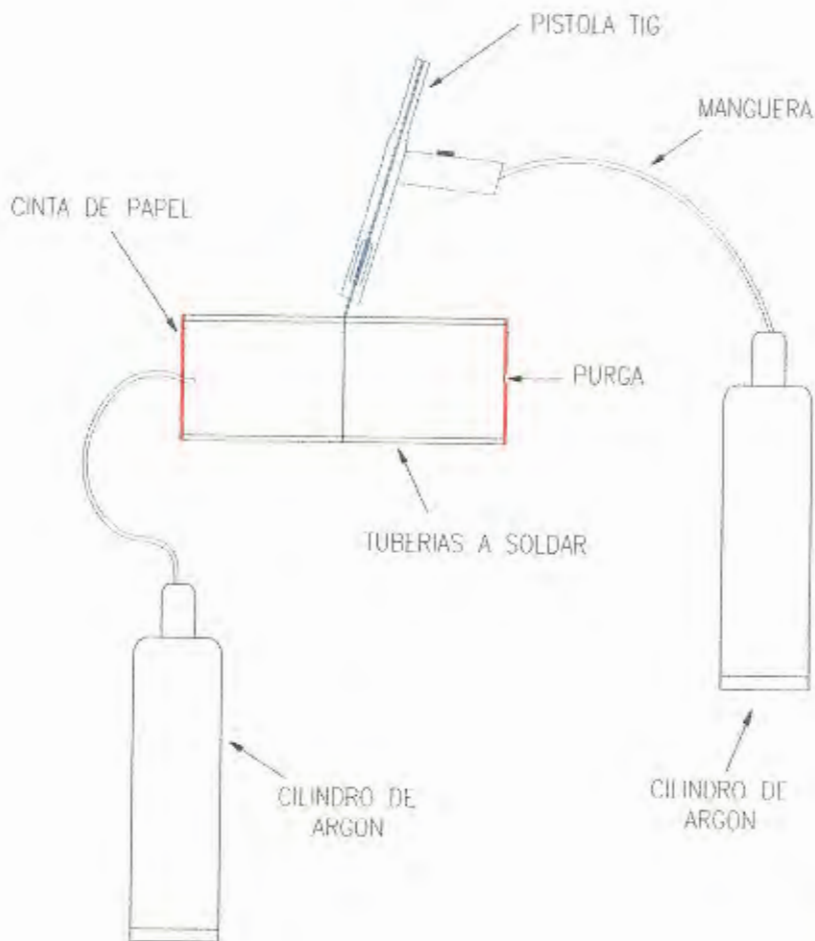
Soldadura de tuberías con proceso TIG barrido interno.
